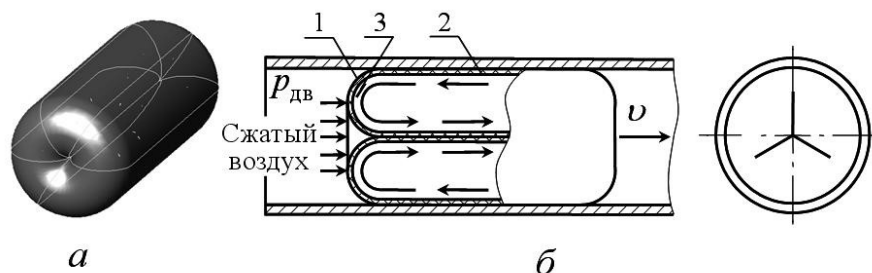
Торообразный привод: *а* – общий вид; *б* – схема движения в трубопроводе; 1 – тканевая оболочка; 2 – резиновая камера; 3 – ниппель
